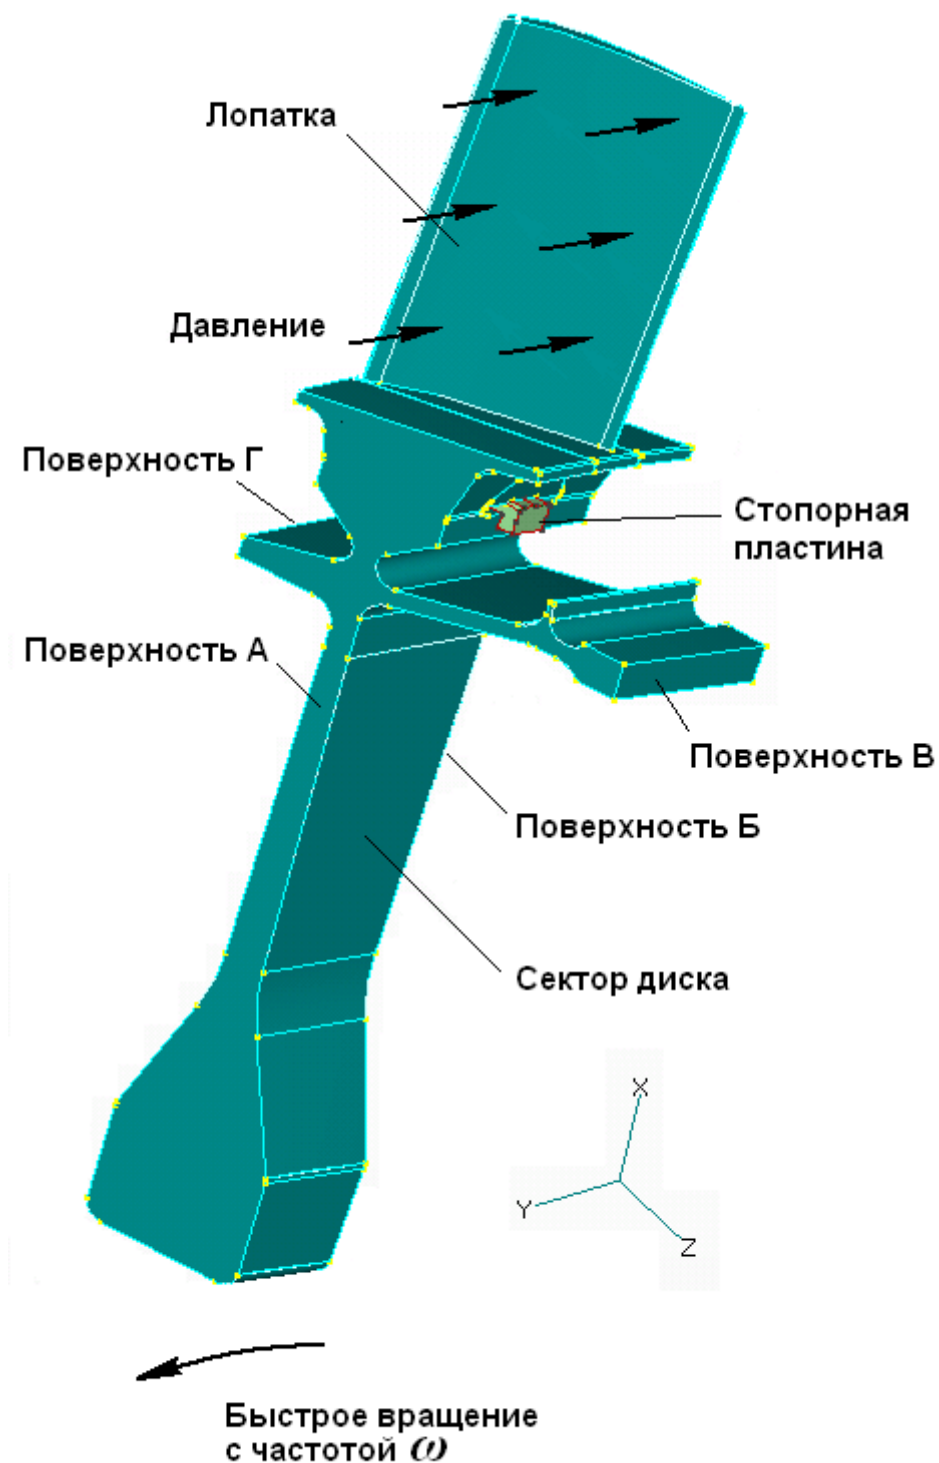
Розрахункова схема диска компресора ТРД з лопаткою
